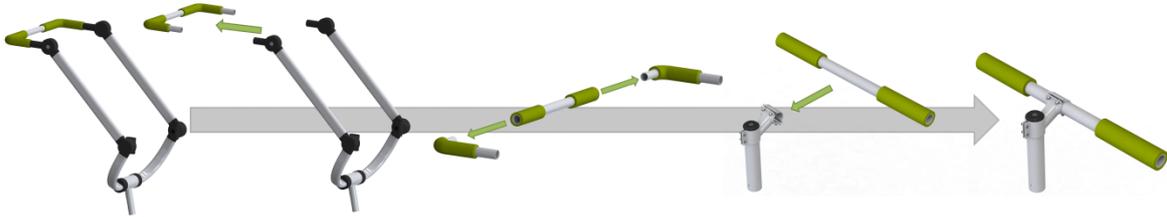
Desmontagem do suporte para empurrar carrinho e montagem do guiador
